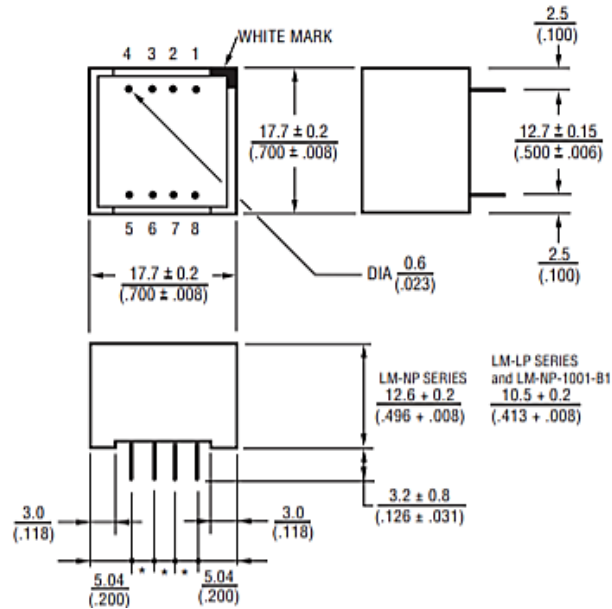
Внешний вид и габаритные размеры LN-NP-1002
